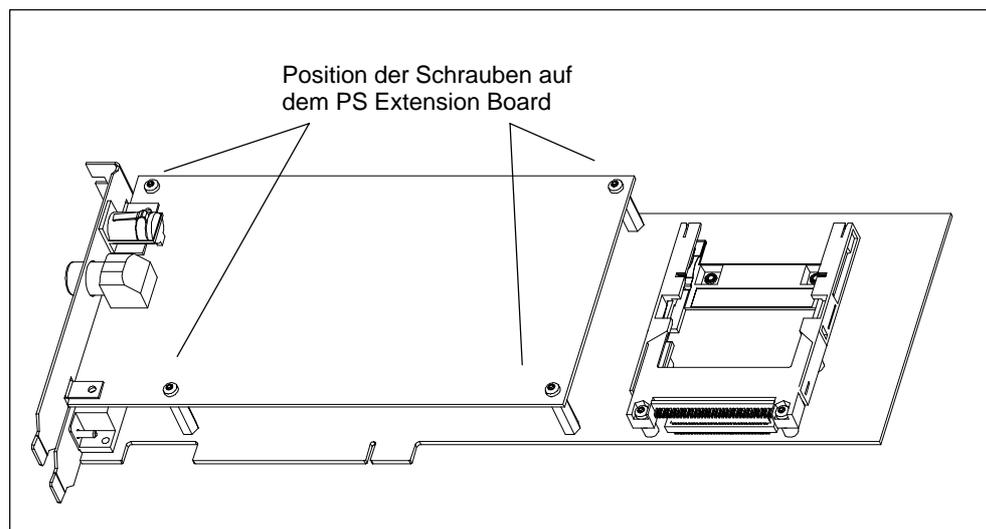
Verschrauben der CPU 41x-2 PCI mit dem PS Extension Board
